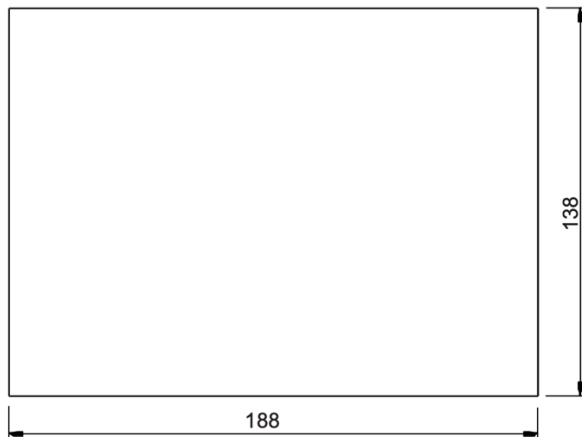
Размеры отверстия для установки контроллера ИВА-128 на щит.
